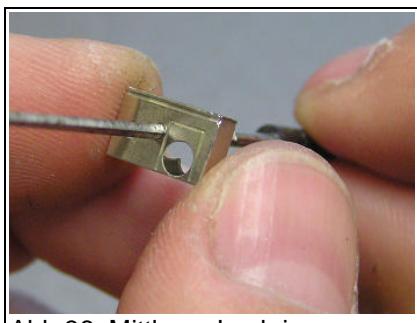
Mittleres Loch im Getriebekasten auf 1,4mm (entspricht Buchsenaußen-durchmesser H1014) aufreiben
